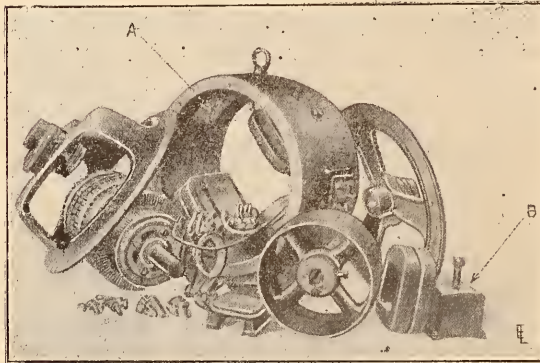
Machine à pôles démontables. — A. Emplacement du pôle rapporté B.
